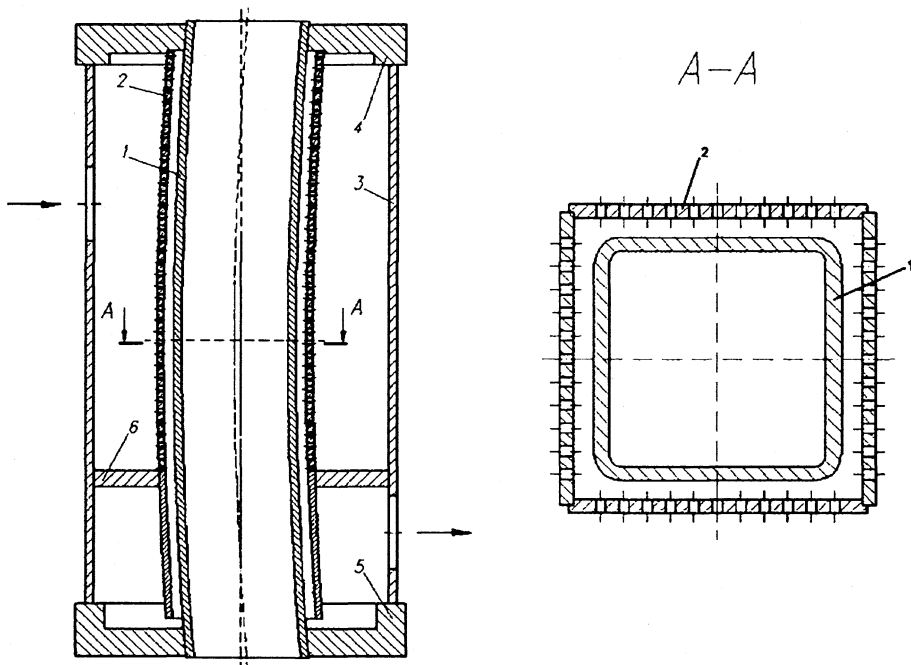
Схема струйного охлаждения кристаллизатора МНЛЗ: 1 – кристаллизатор; 2 – экран; 3 – цилиндр; 4 – верхний фланец; 5 – нижний фланец; 6 – перегородка
